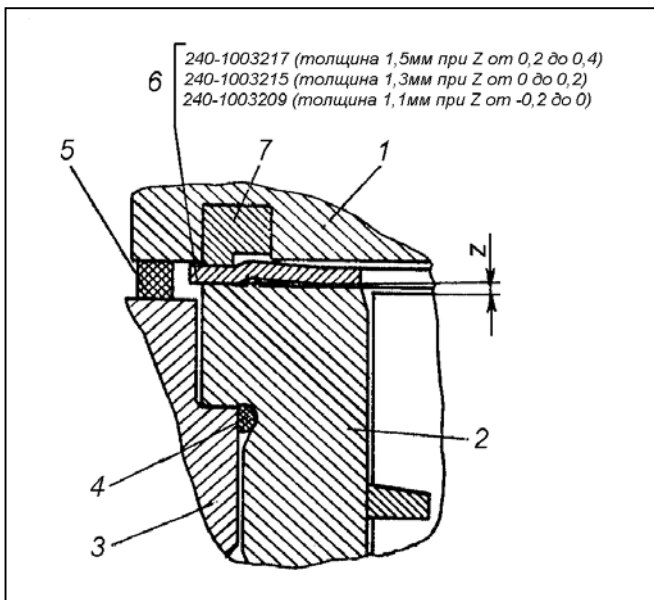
К установке головки цилиндра двигателя ЯМЗ-240БМ:
